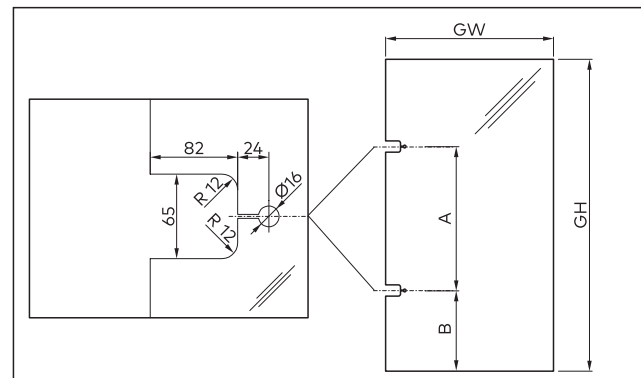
Glasbearbeitungen für die Zargenbefestigung mit einglassener Montageplatte
